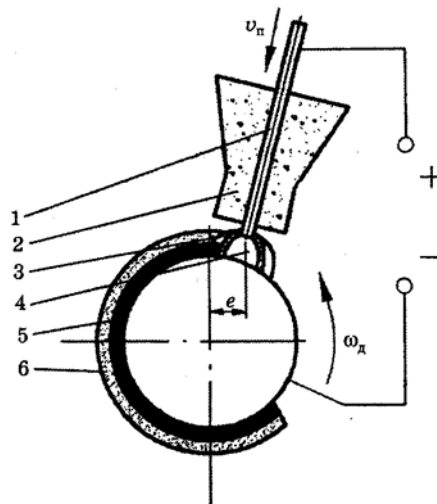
Схема наплавлення під шаром флюсу:
